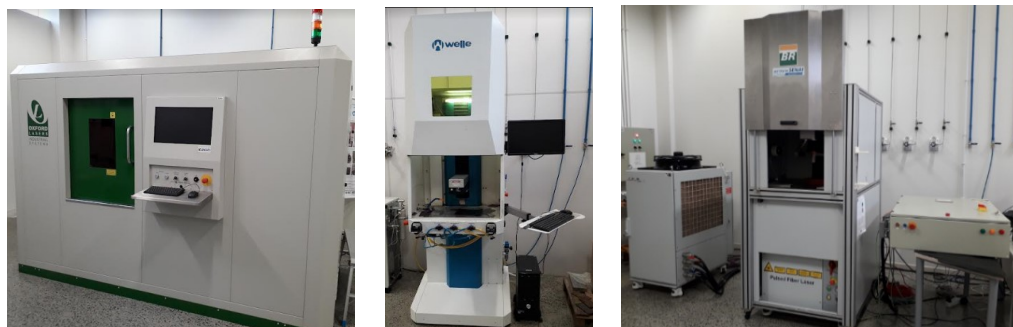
PRECO (máquina à esquerda) e Welle Laser 1 (máquina à direita)
